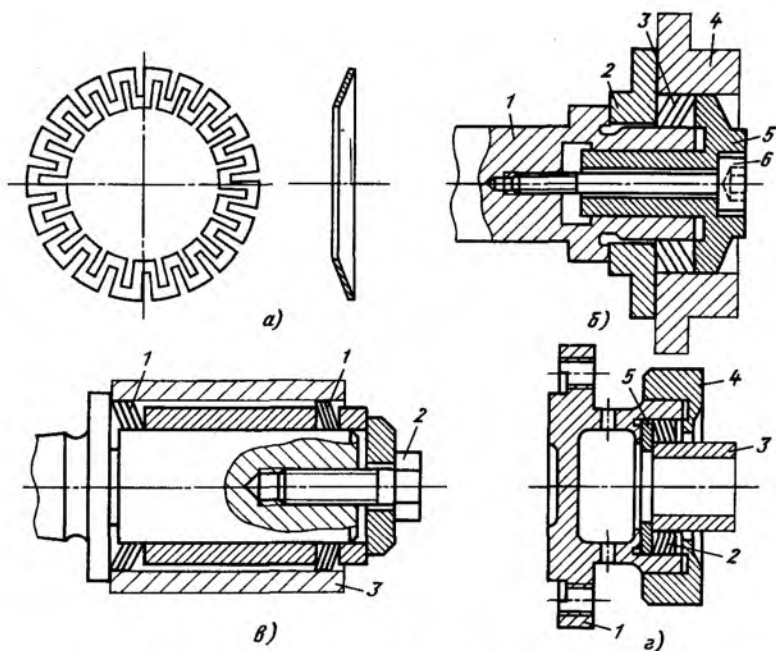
Оправки и патроны с тарельчатыми пружинами:
